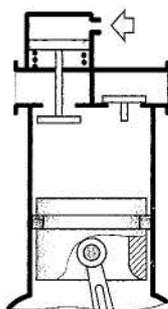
Управление принудительным отжатием всасывающего клапана компрессора
